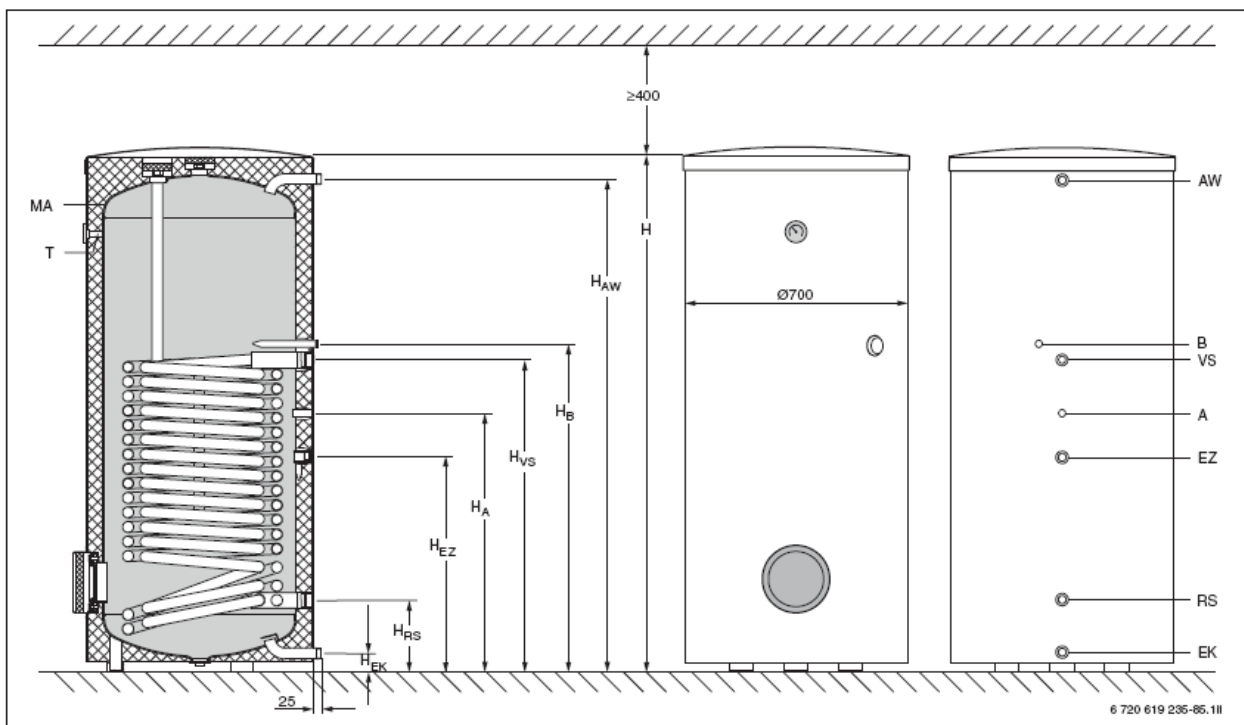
Габаритные размеры баков-водонагревателей SH290 RW, SH370 RW и SH400 RW (размеры в мм)
